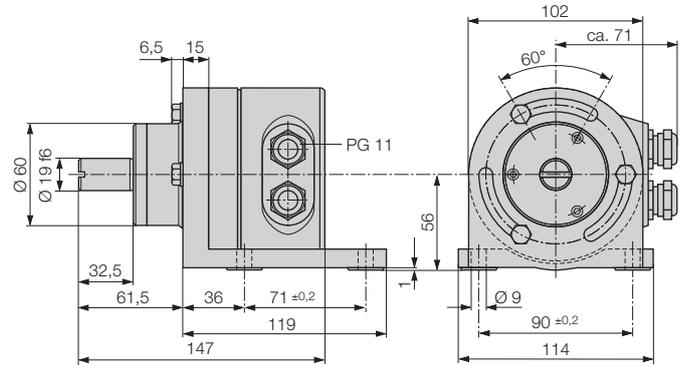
KINAX WT 707 mit Schraubklemmen sowie Stopfbuchsen und Fuss.
